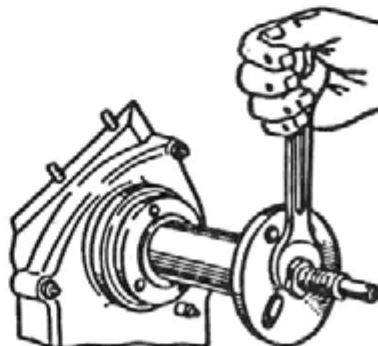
Напрессовка ступицы шкива коленчатого вала с помощью приспособления 16-У-236817
